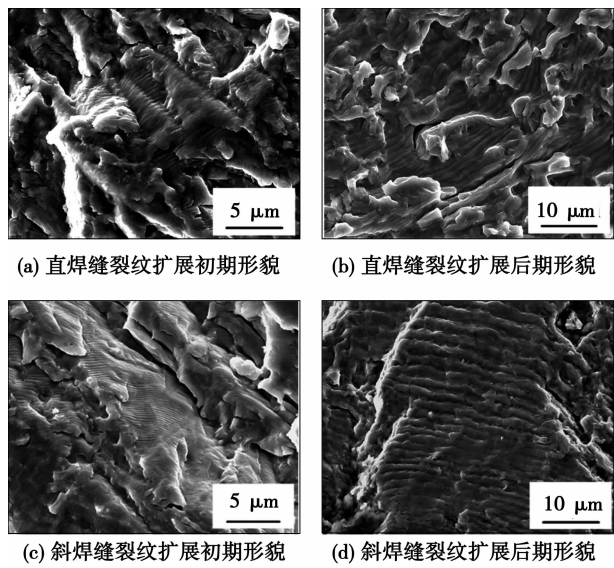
激光直、斜焊缝试件疲劳裂纹扩展区断口形貌
